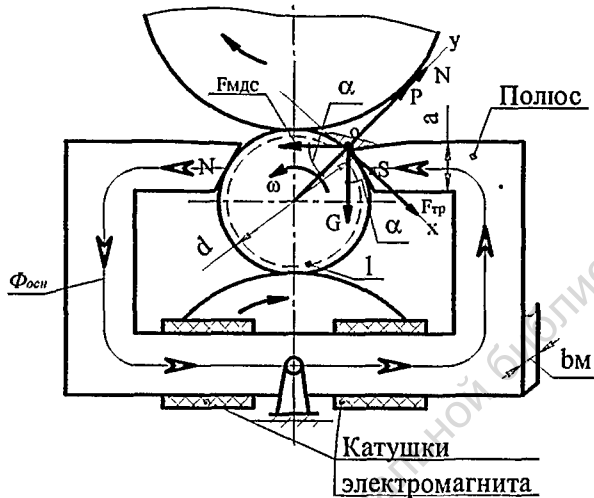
Схема сил, действующих на частицу металлического порошка в момент отсутствия импульса сварочного тока
